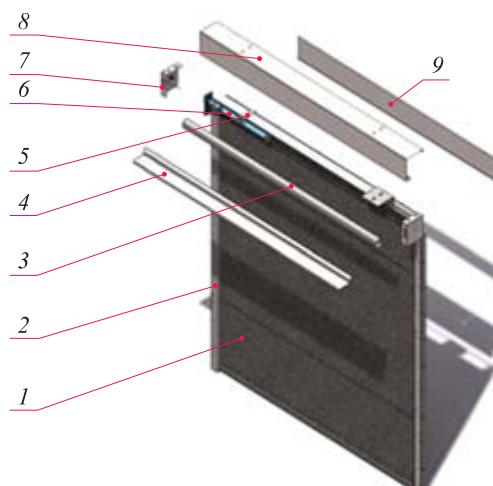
Пример конструктивного исполнения противопожарных штор с управлением электронной автоматической системой: 1 — полотно; 2 — боковая шина; 3 — вал; 4 — направляющая полотна; 5 — монтажный элемент (пластина или уголок); 6 — внутривальный двигатель; 7 — боковая крышка; 8 — кожух; 9 — задняя крышка
